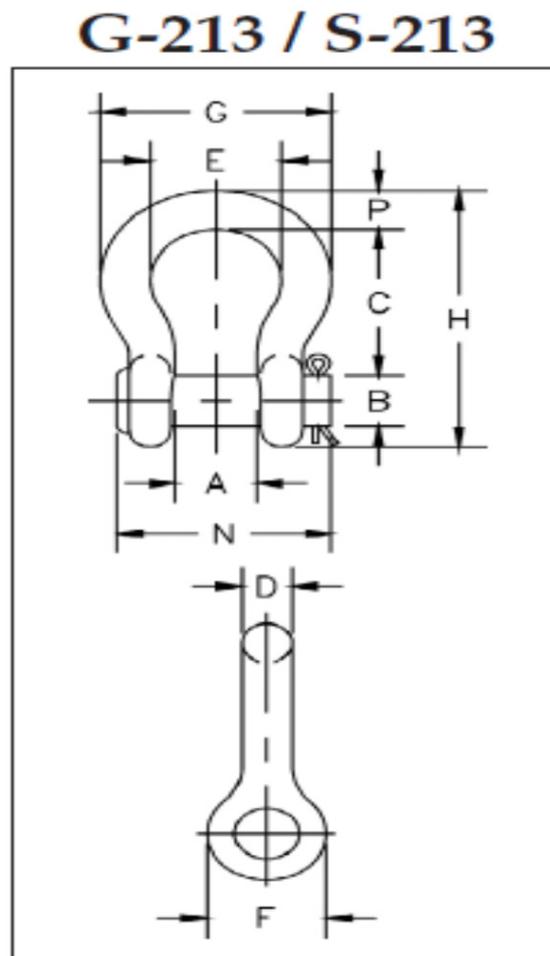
Dimensiones principales de la argolla (ref. 7)
